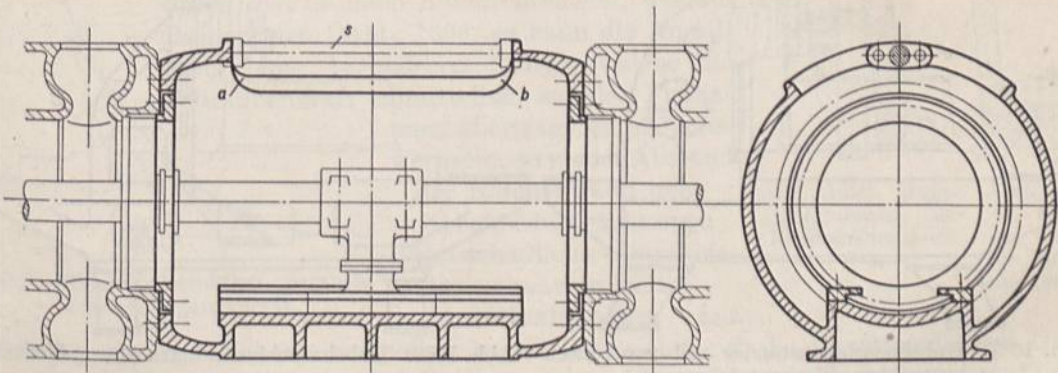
Zwischenstück mit Ausschnitt oben.
